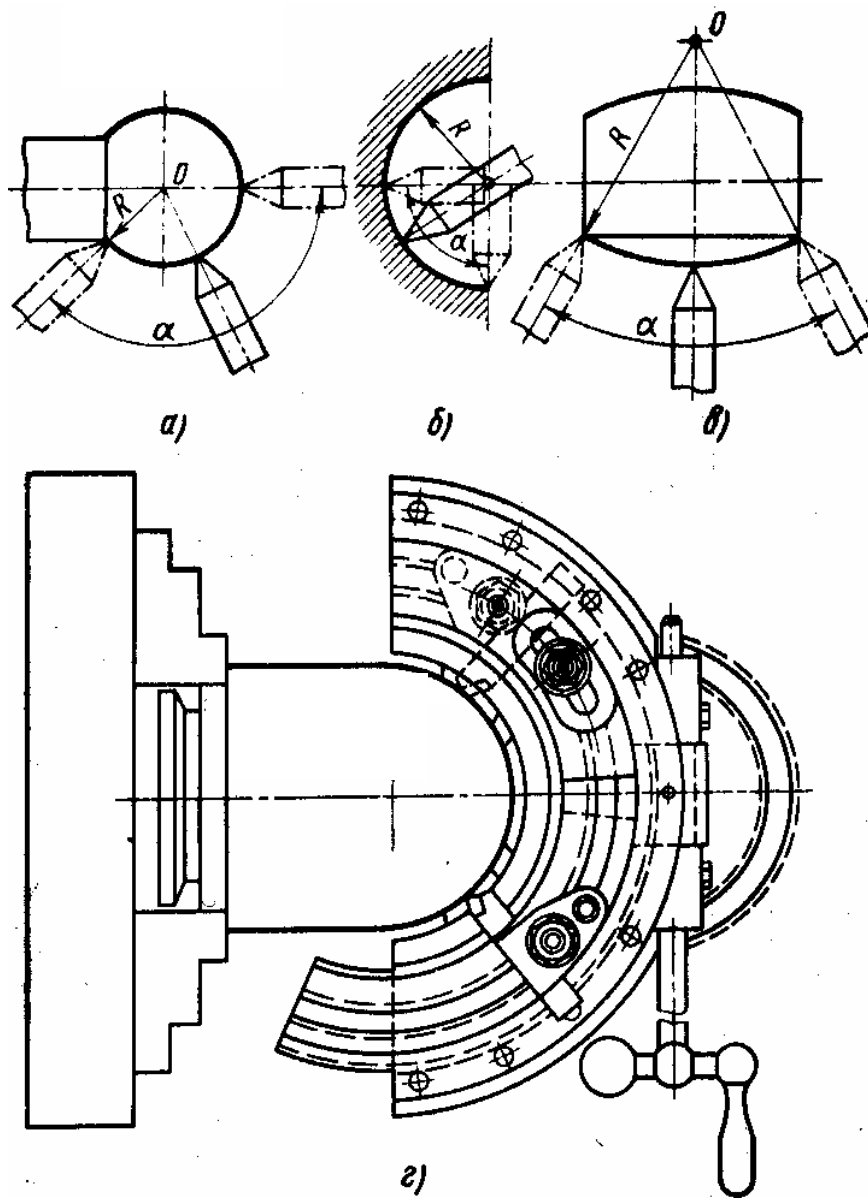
Схеми обробки фасонних поверхонь заготовок
